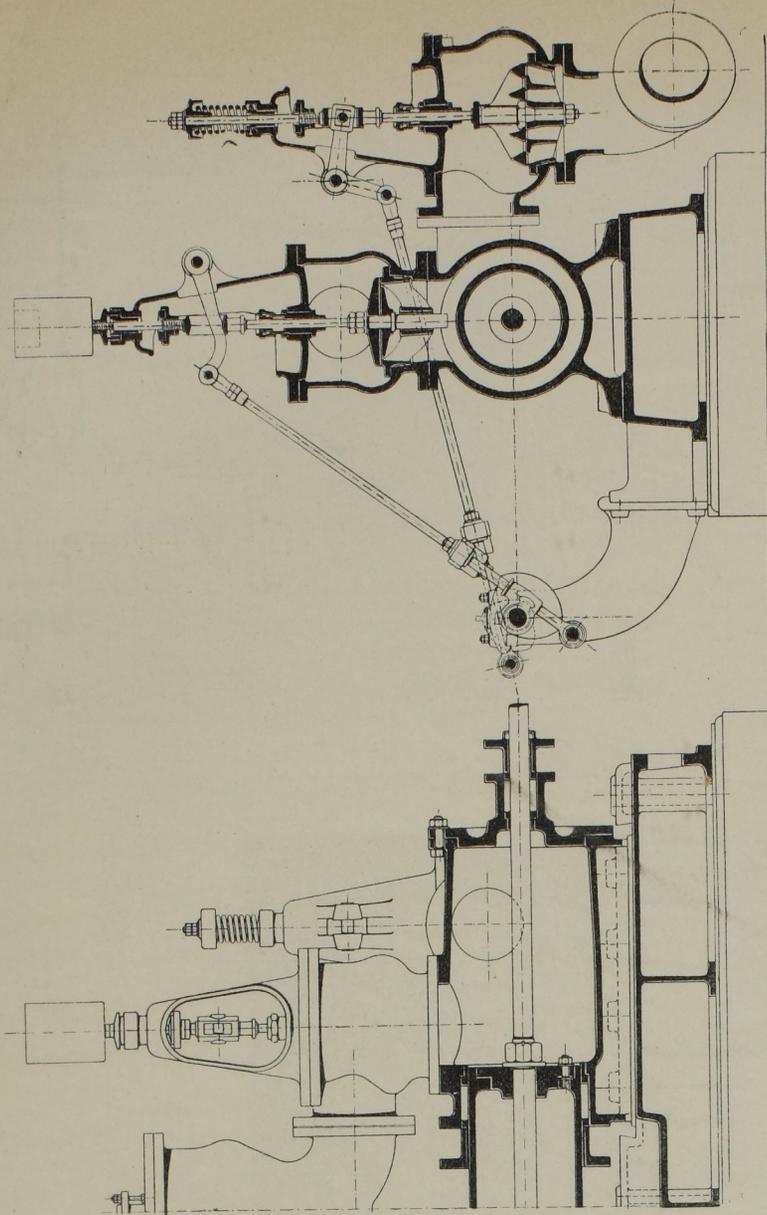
Steuerung der Pumpe für 4 cbm. Masst. 1 : 25.
